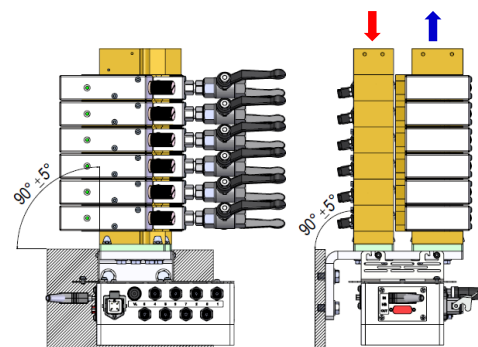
Posición de montaje vertical, ej. versión izquierda
